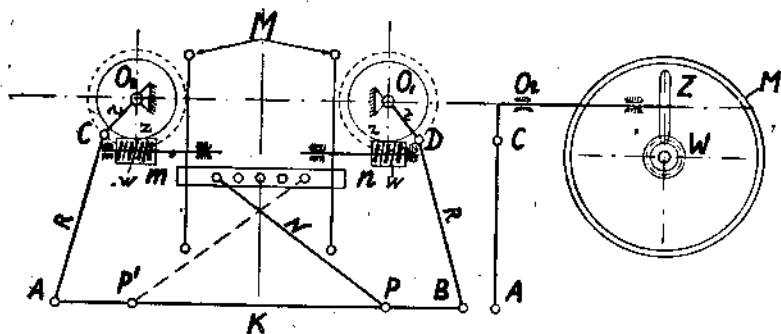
Схема механизма заглубления ножа грейдеров „Патроль“ и „Беджер“.
